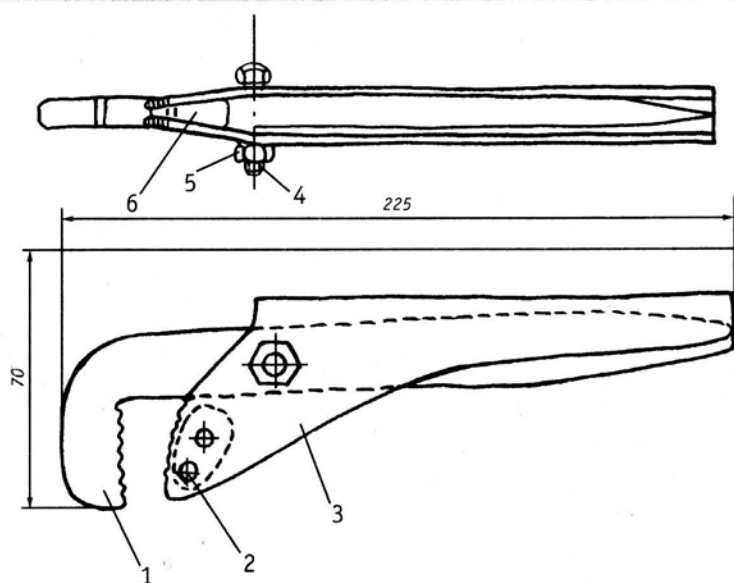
Ключ трубный переставной двухрычажный английского типа: 1 — подвижный рычаг; 2 — заклепка; 3 — неподвижный рычаг; 4 — болт; 5 — гайка; 6 — «сухарь»
